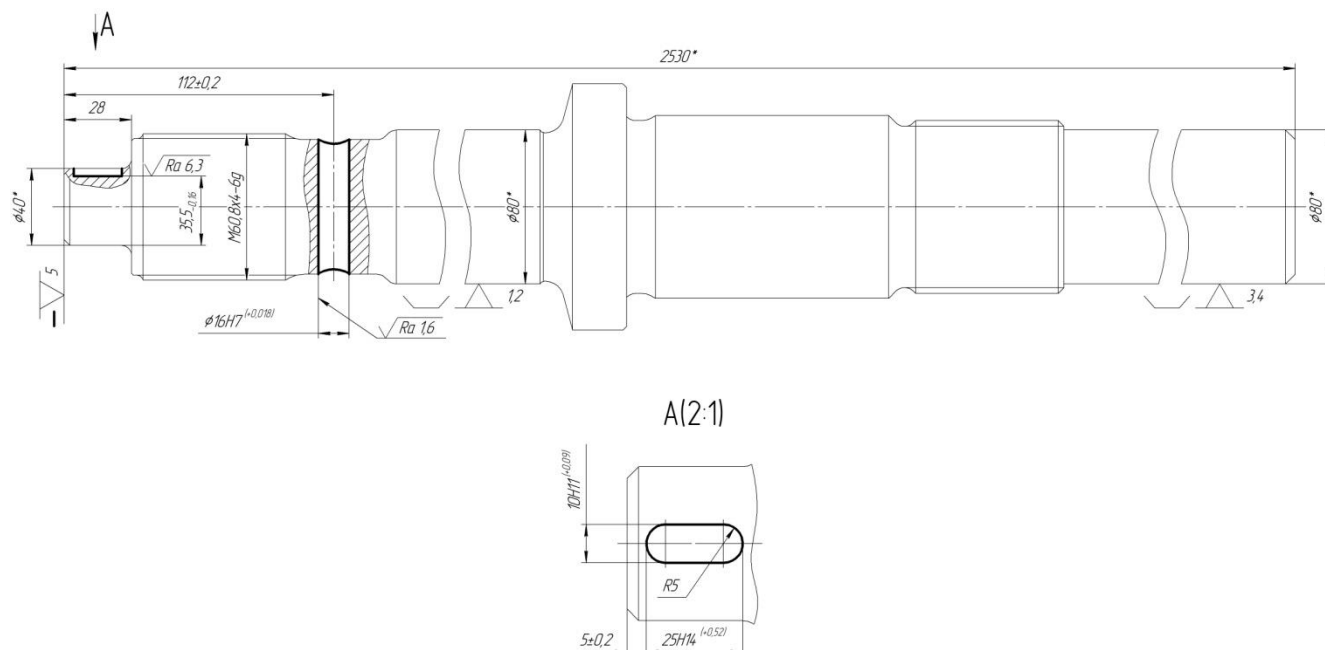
Схема базування заготовки на комплексній з ЧПК операції
